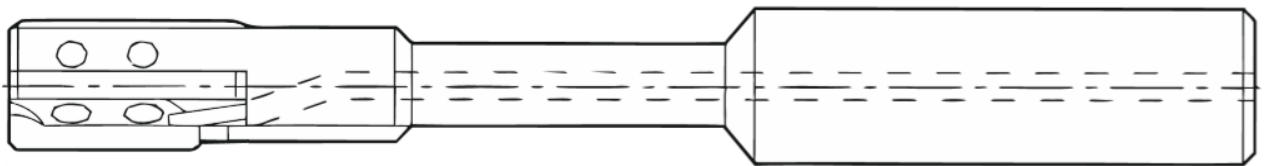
Розвертка “Bifix SR80” зі змінними ножами [8, ст.294]
